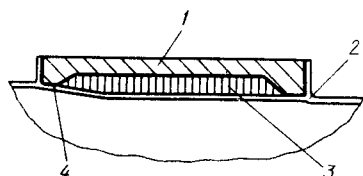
Корпус вентилятора, удерживающий лопасти при их отрыве:
